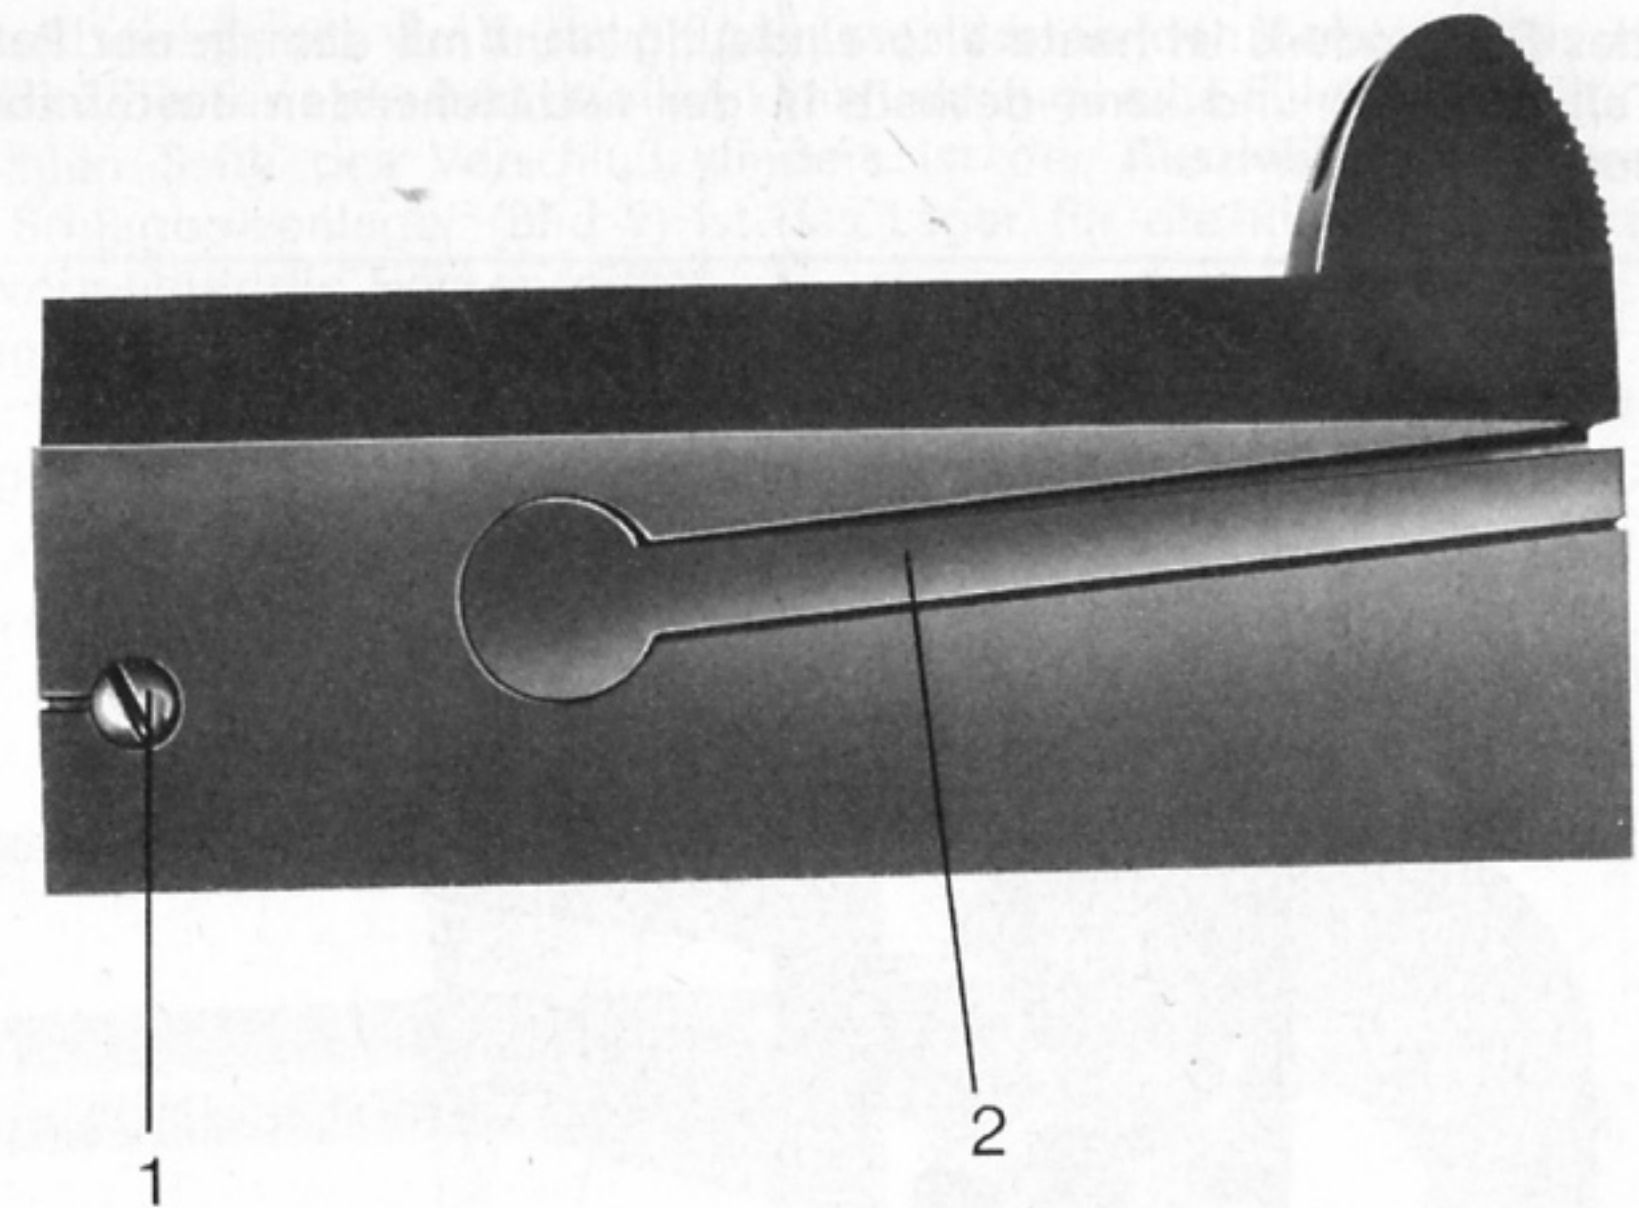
Verschußzylinder von rechts: 1 = Konterschraube (Nr. 5 von Bild 7), 2 = Auszieher.
